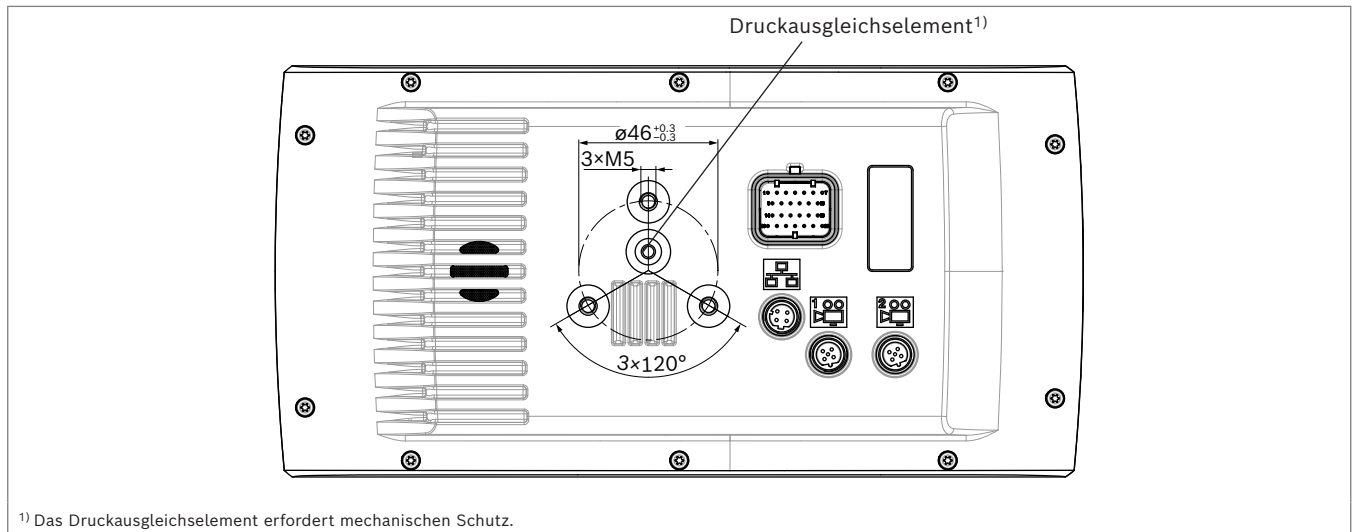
Ausschnitt für Einbau eines DI4 in ein Armaturenbrett
